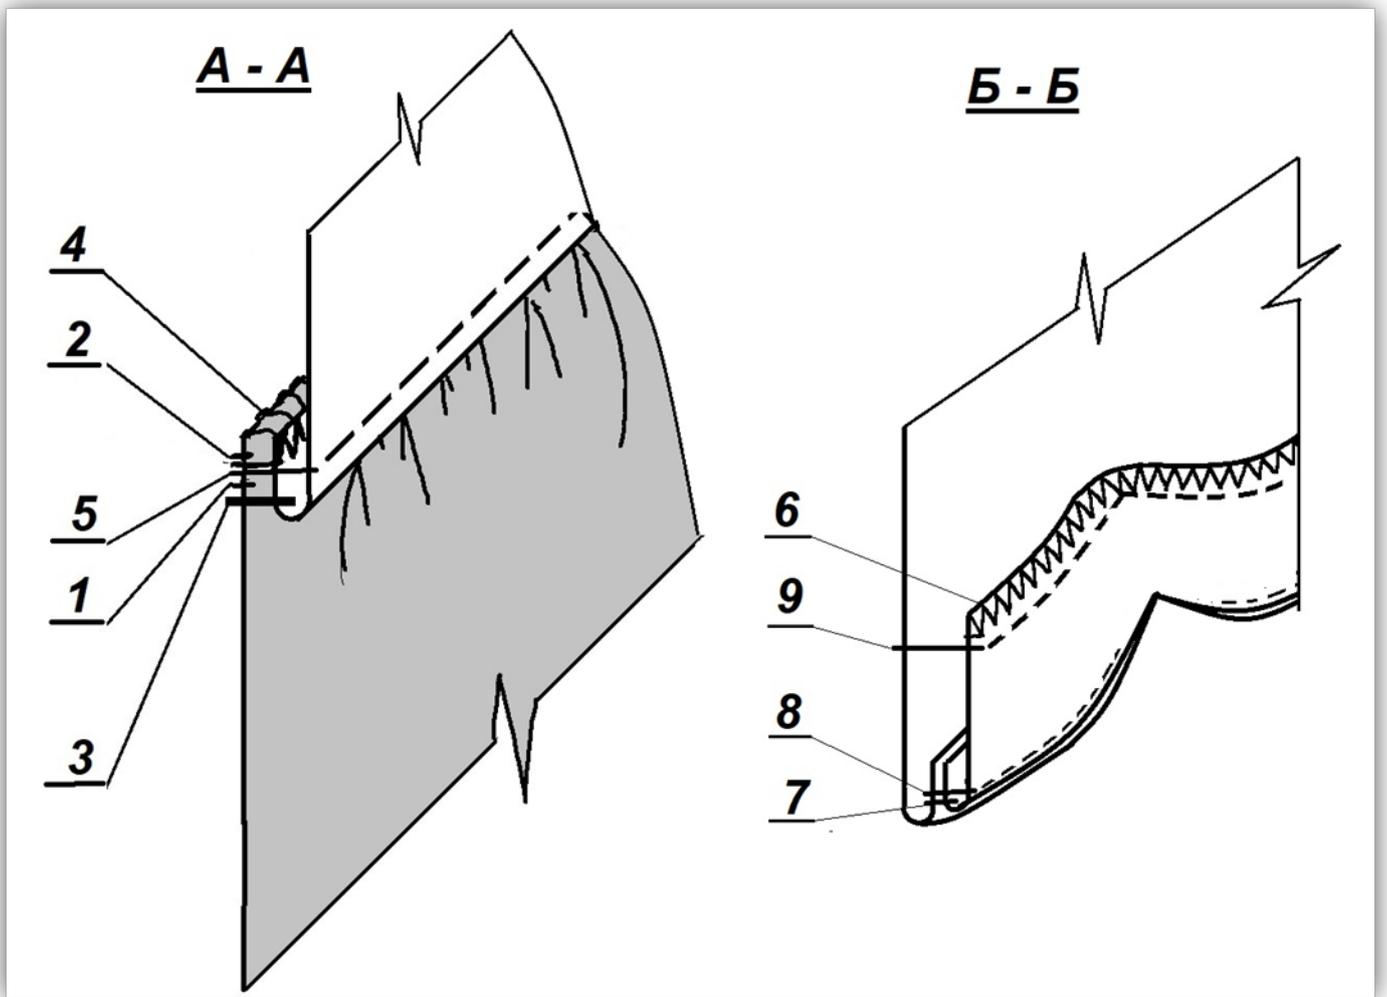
Схема соединения кокетки и обработки низа ПШЮ
